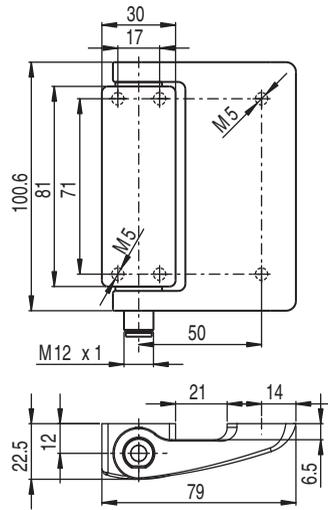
Dimensões do S410-M1M12-B em mm
